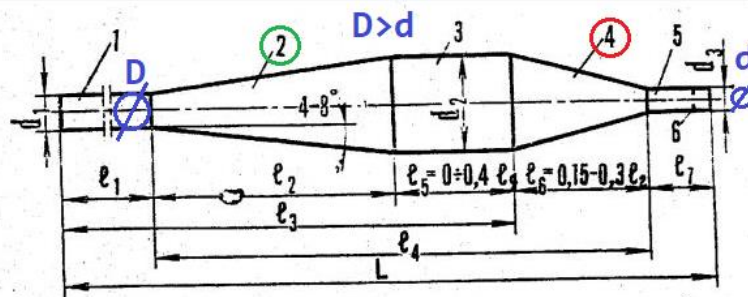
Система выпуска и исходные размеры ее элементов: 1 — выпускная труба; 2 — диффузор (конус расширения); 3 — цилиндрическая часть; 4 — конфузор (конус сжатия); 5 — выходная труба глушителя; 6 — шайба
